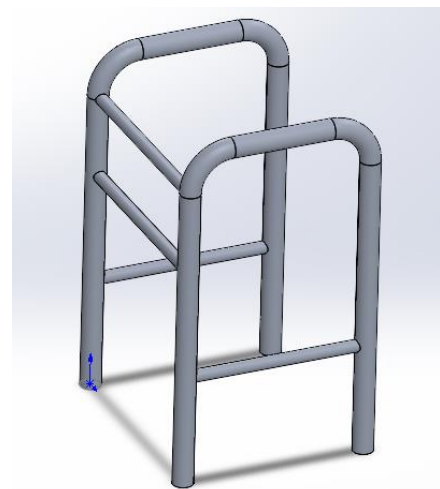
Caminador geriátrico sólido- Vista Isométrica.
